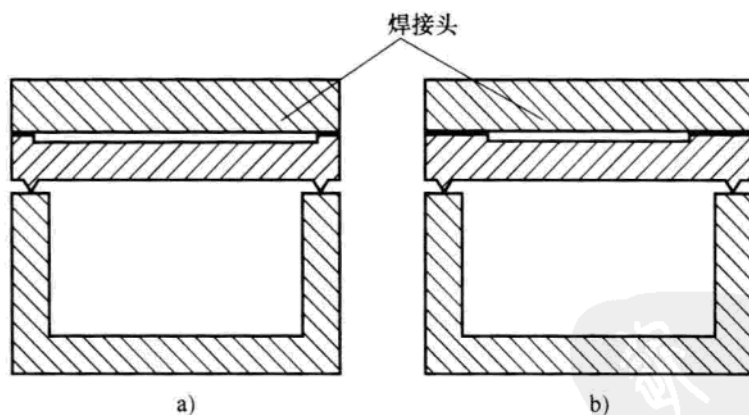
增加塑胶件焊接面与焊接头的接触面积
